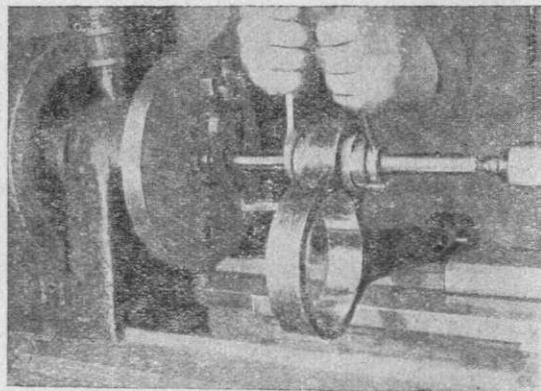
Процесс расшлифовки проушины главного шатуна мотора М-17 на токарном станке.
